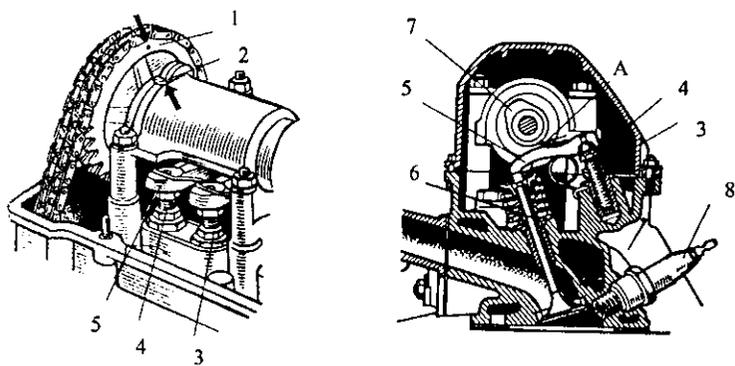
Механизм газораспределения (ВАЗ-2106):
